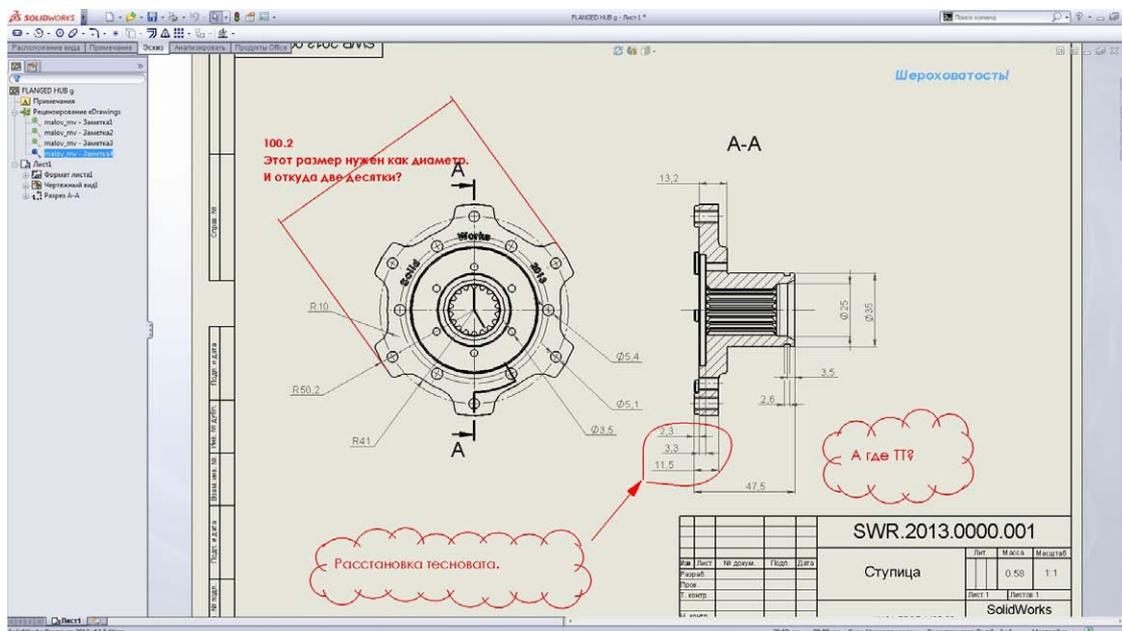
, Заметки eDrawings в чертеже SolidWorks.
